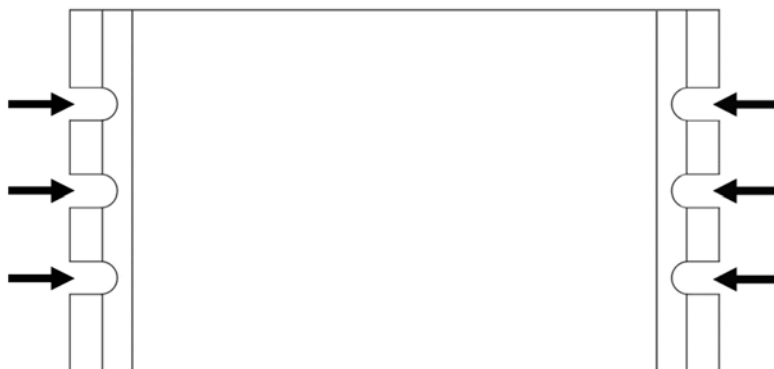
C-863.11: Montageleisten mit Aussparungen (siehe Pfeile)
